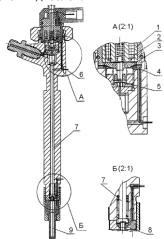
ЭГФ с датчиками перемещения якоря УК (А) и иглы распылителя (Б): 1 — магнитопровод; 2 — обмотка; 3 — якорь; 4 — датчик якоря; 5 шариковый управляющий клапан; 6 — плунжерный мультипликатор запирания; 7 — штанга мультипликатора; 8 — датчик иглы; 9 — игла распылителя.
